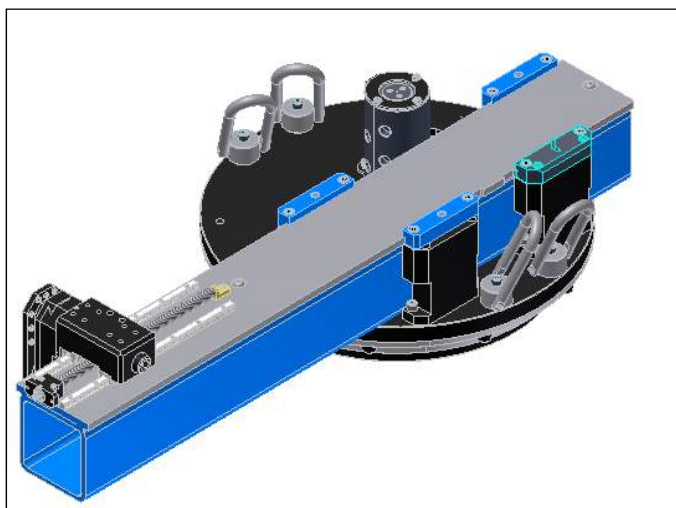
Поворотный стол и рычаг патрона для обработки внешних диаметров в сборе
